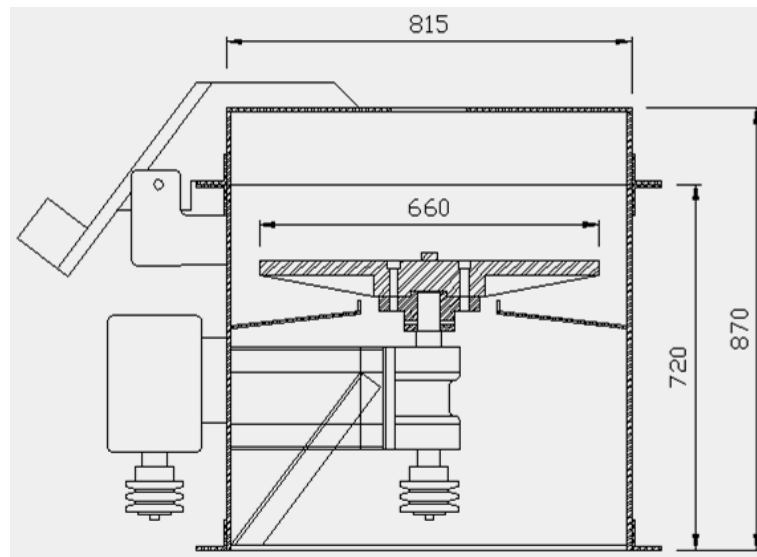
ESQUEMA DE LAS DIMENSIONES DE LA MÁQUINA
